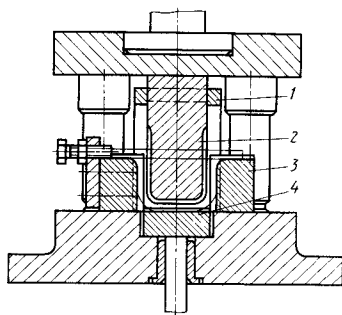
Штмп с жестким съемником для U-образной гибки заготовки из прутка
